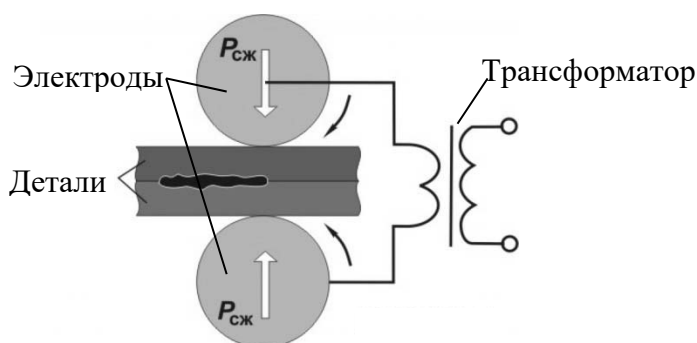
Схема роликовой сварки давлением
